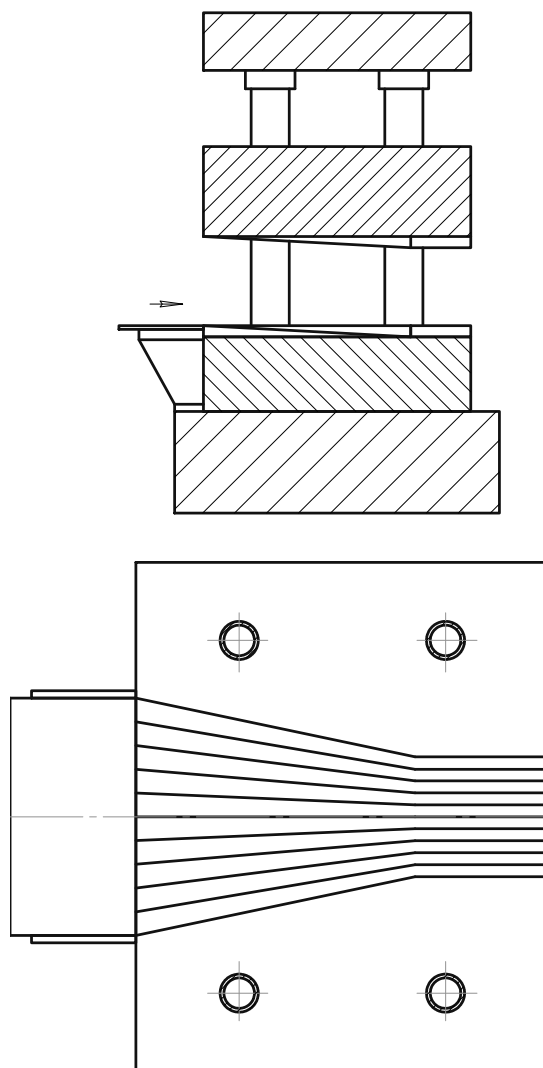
Штмп для виготовлення гофрованої стрічки
